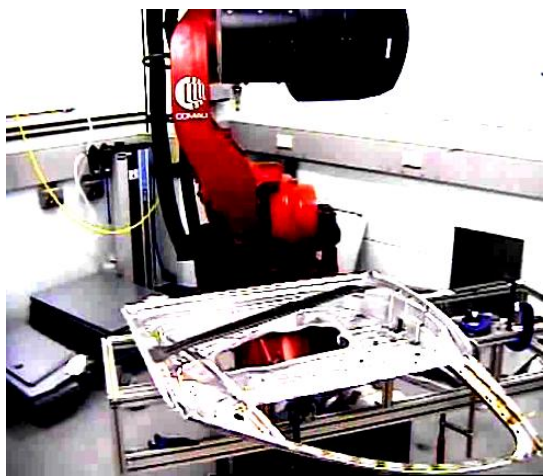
Российская установка для лазерной сварки стальной металлоконструкции дверей легкового автомобиля [3]
